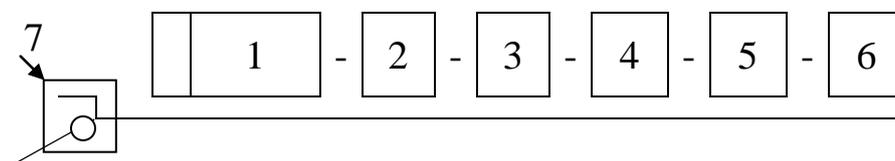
Обозначение сварных швов по ГОСТ 2.312-72.
